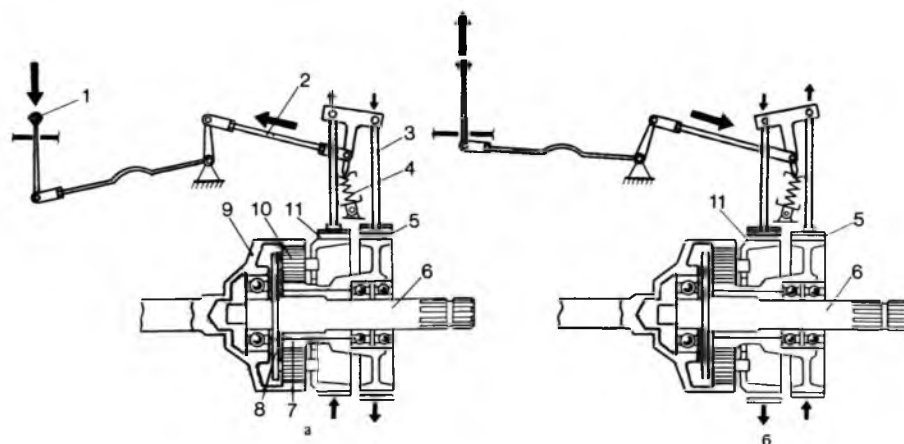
а, б – Схема работы ВОМ с планетарным редуктором
